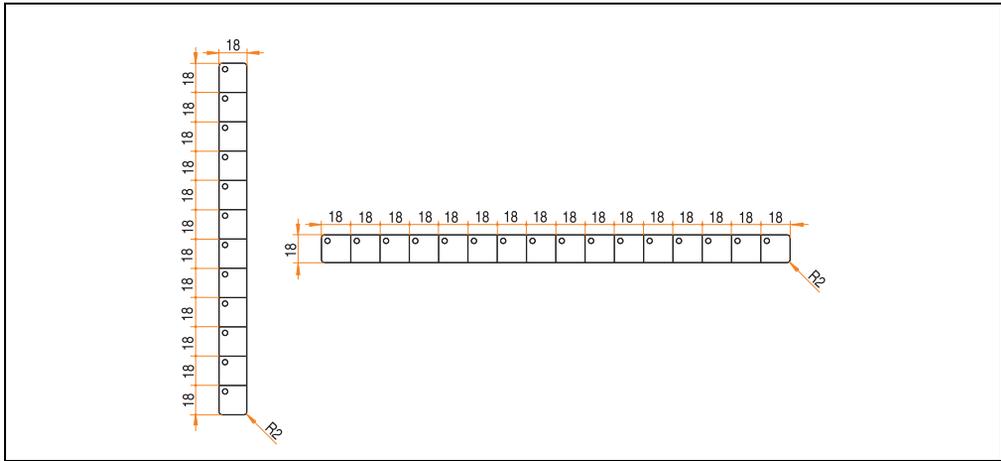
Tastenabmessungen - 5AP880.1505-00
